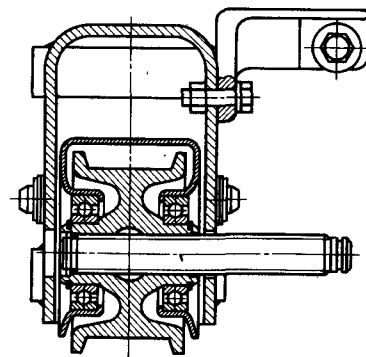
Схема установки ходового колеса в коробке, встроенной в концевую балку
